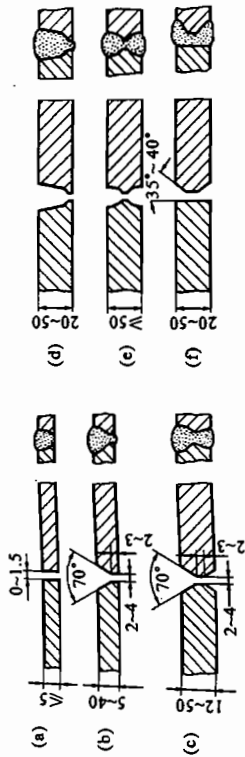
坡口形式及其适用的焊接件厚度(单位为 mm)
